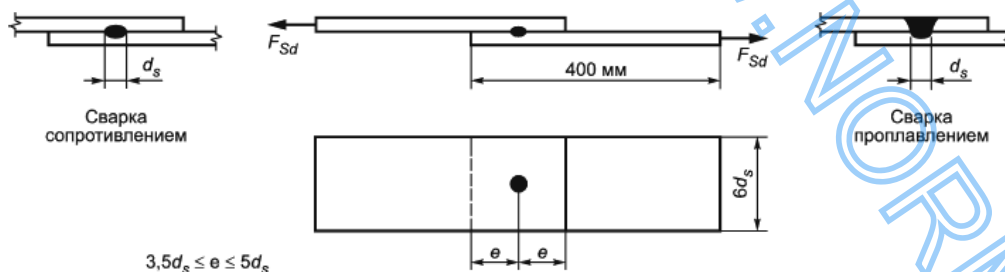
Образцы для испытаний на срез сварных точек
